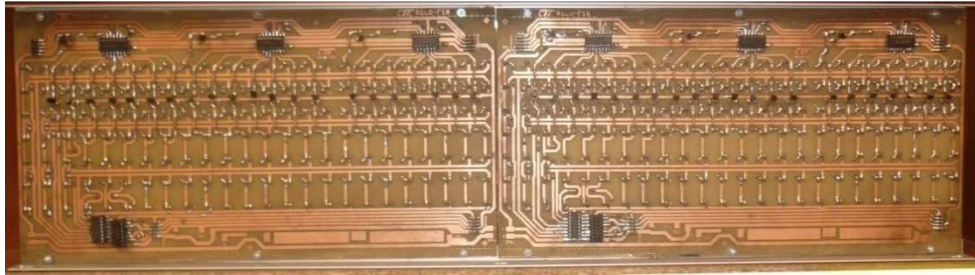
Ensamblaje del Rótulo lado de Pistas y Elementos
